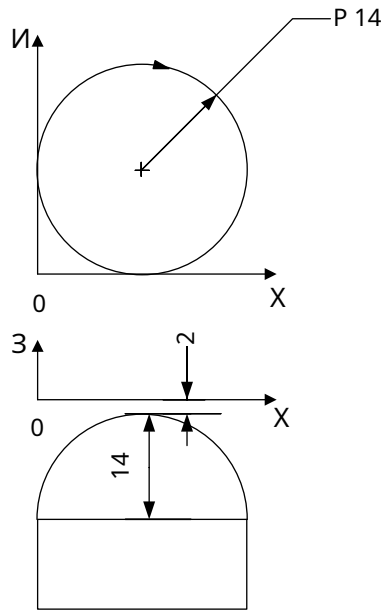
Эскиз 6 процесса обработки заготовки
